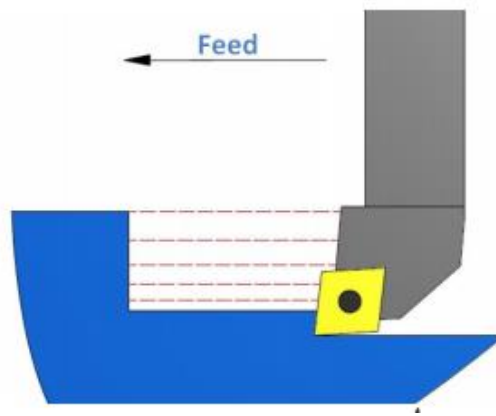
Траєкторія руху вершини інструменту при зменшенні глибини різання із наближенням різця до остаточної поверхні обробки [25]
